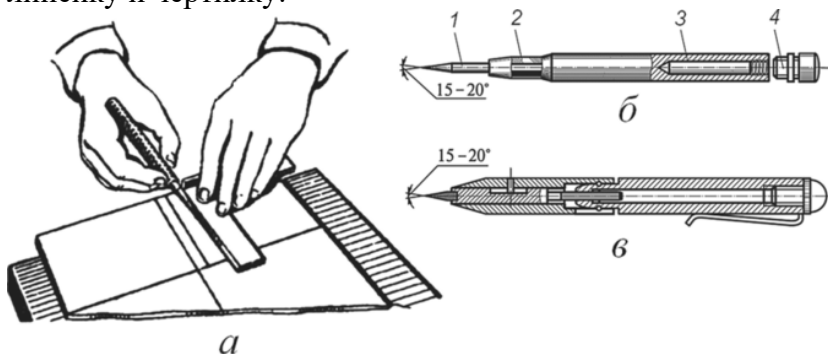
Нанесение рисок с помощью чертилки: а — прием работы; б — круглая чертилка; в — чертилка со вставной иглой; 1 — игла, 2 — корпус, 3 — запасные иглы, пробка
